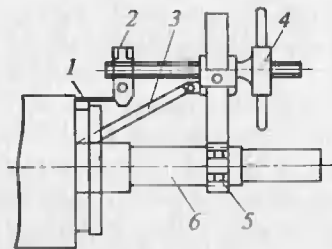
Приспособление для извлечения стержней из пазов ротора:
